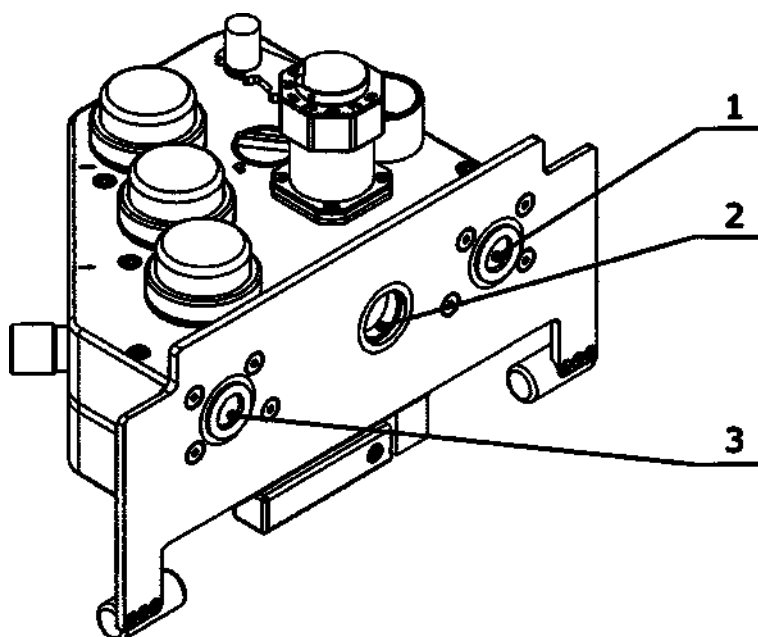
Дыхательный блок, вид со стороны пластины крепления
